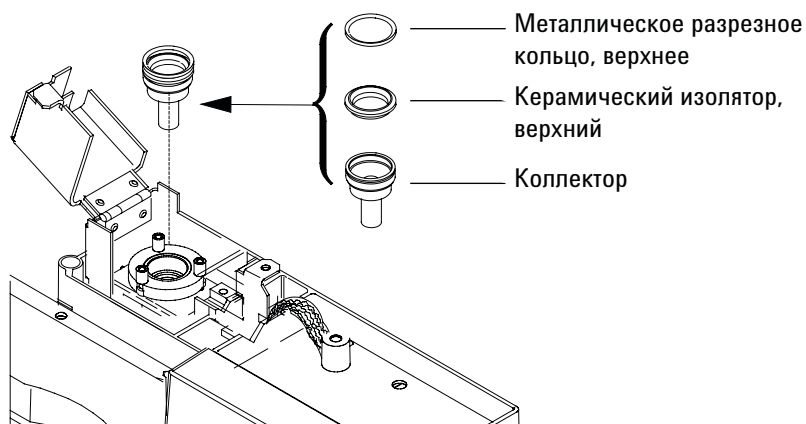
Коллектор АФД, верхний изолятор и металлический кольцевой уплотнитель.
